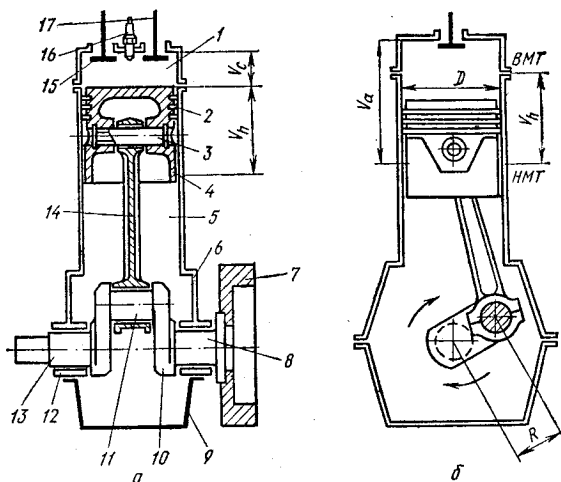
Схема будови поршневого двигуна внутрішнього згоряння: а — поздовжній вигляд; б — поперечний вигляд; 1 — головка циліндра; 2 — кільце; 3 — палець; 4 — поршень; 5 — циліндр; 6 — картер; 7 — маховик; 8 — колінчастий вал; 9 — піддон; 10 — щіка; 11 — шатунна шийка; 12 — корінний підшипник; 13 — корінна шийка; 14 — шатун; 15, 17 — впускний і випускний клапани; 16 — форсунка
